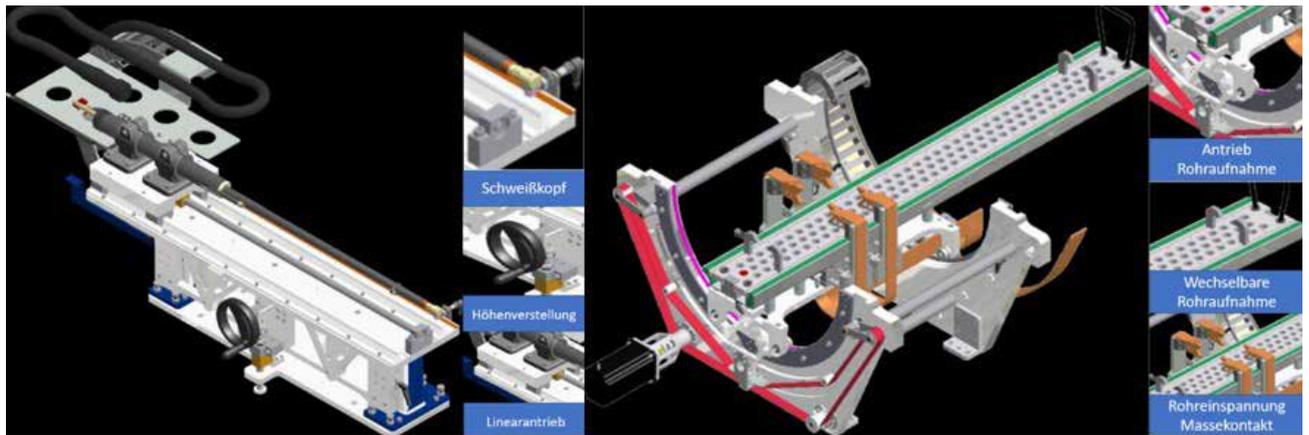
Schweißlanze (links) und Rohraufnahme (rechts)
